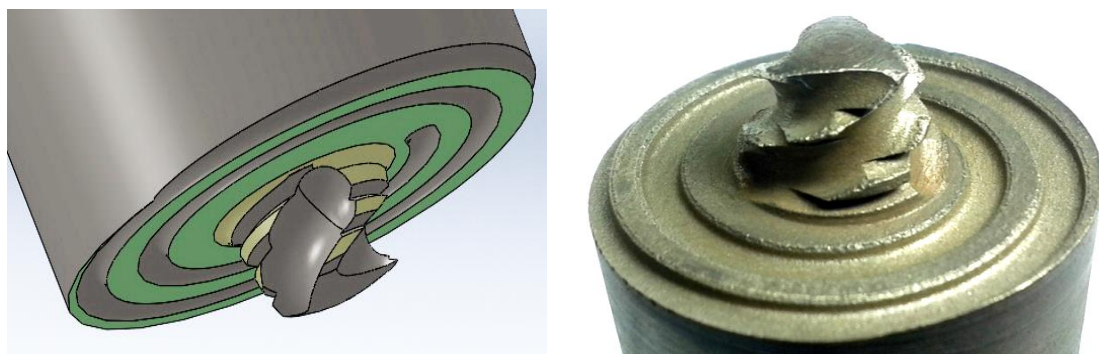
Твердотельная модель и опытный образец инструмента СТП с рабочей частью спиралевидной формы
